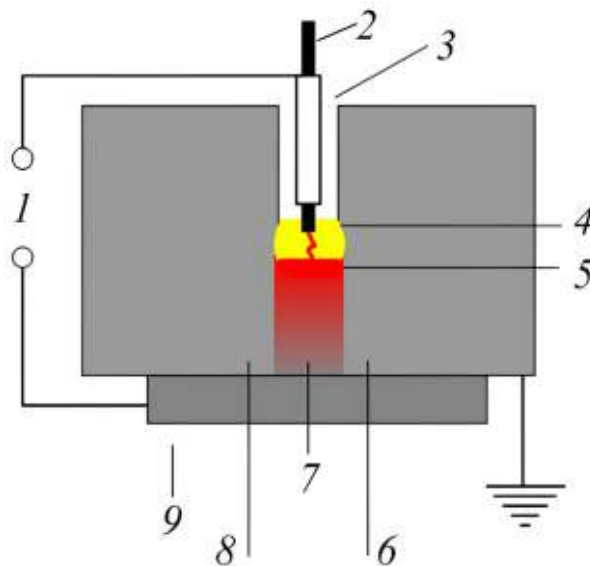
Схема электрошлаковой сварки. 1 – источник питания, 2 – плавкая проволока; 3 – направляющая трубка, 4 – шлаковая ванна, 5 – металлическая ванна; 6, 8 – свариваемые детали, 7 – сварной шов, 9 – подкладная плита.
